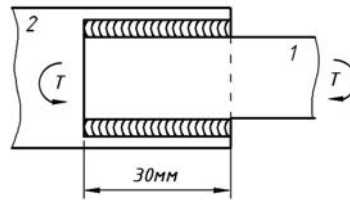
Сварное соединение полосы с косынкой
